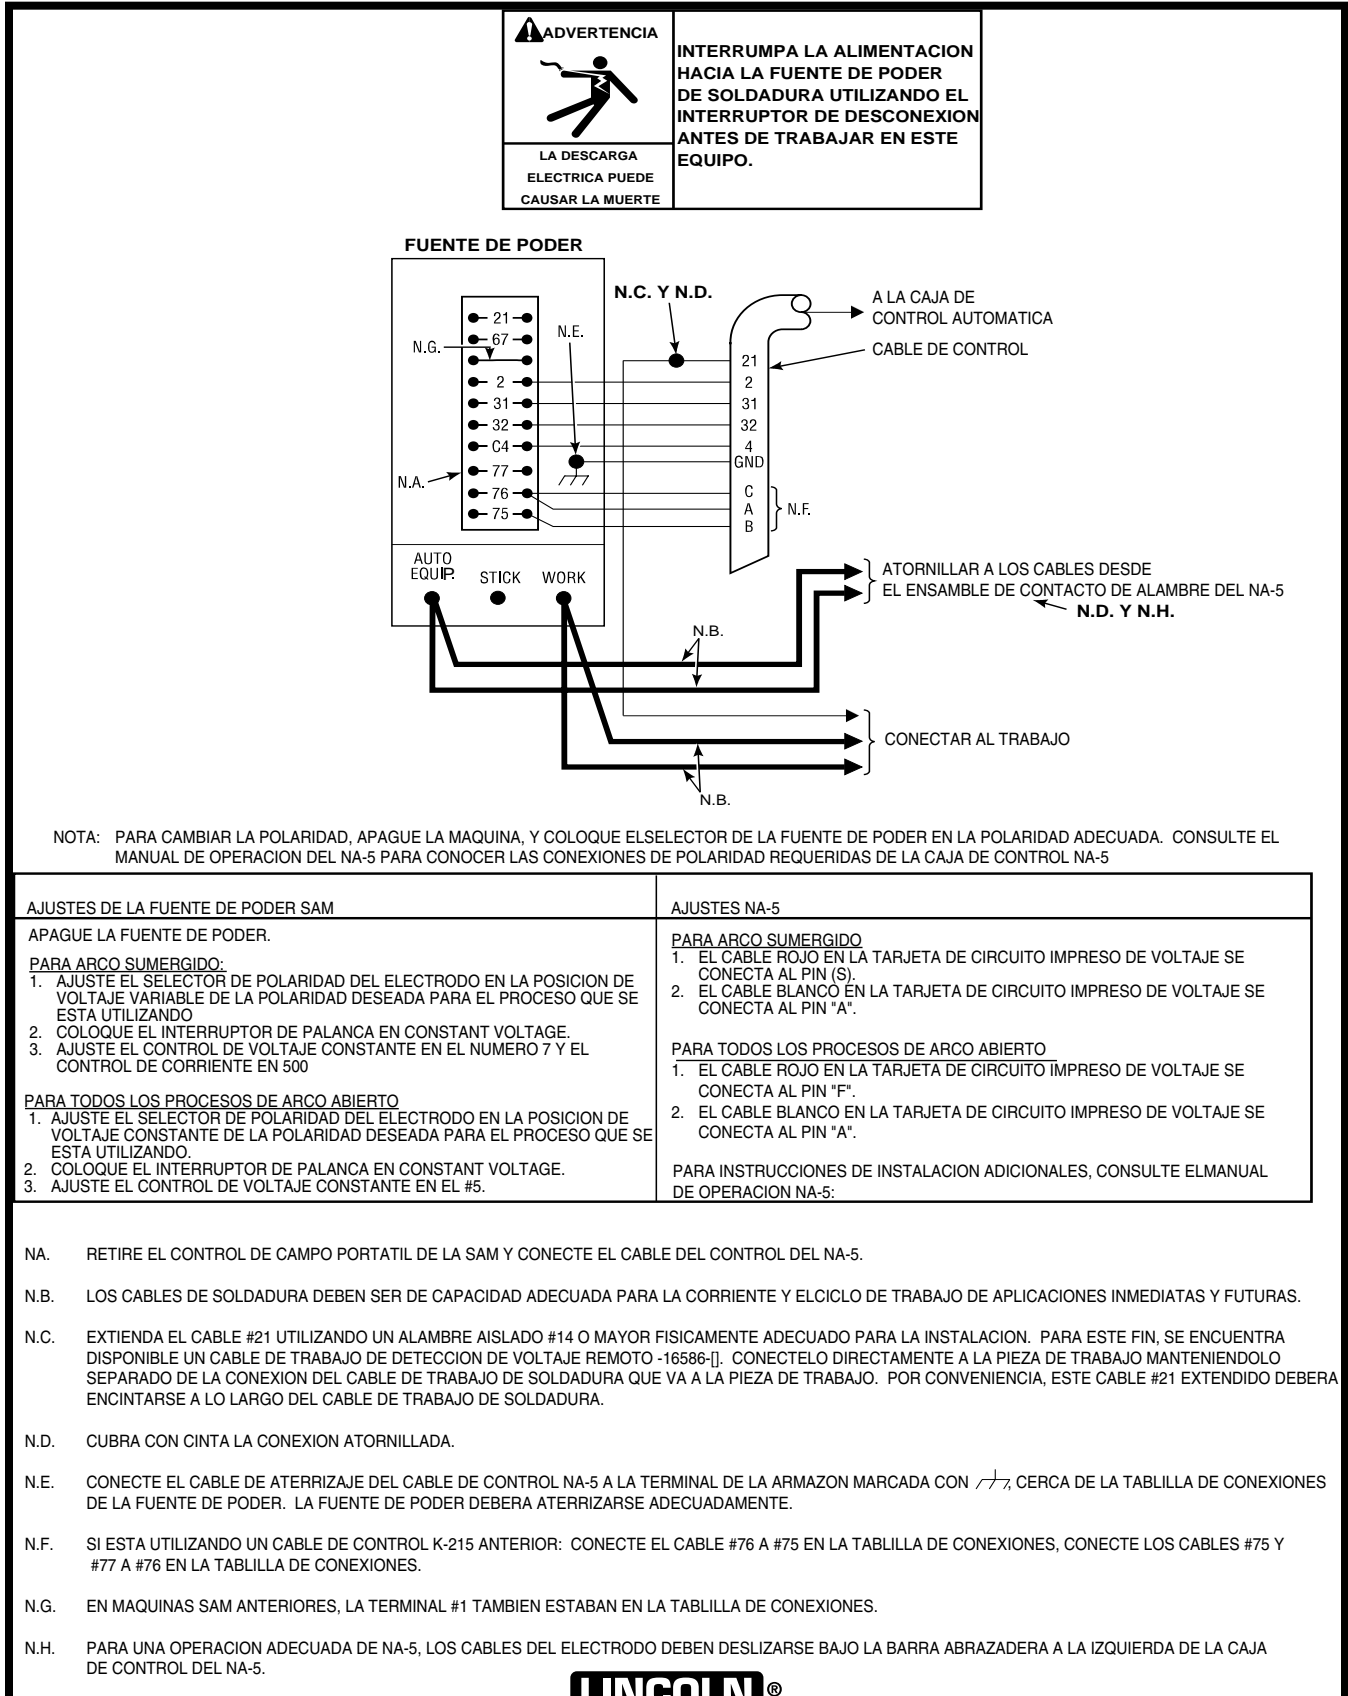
CONEXIÓN DEL NA-5 (TODOS) A UN GENERADOR DE MOTOR ELECTRICO SAM – 400 O SOLDADORA DE MOTOR DE COMBUSTION.
